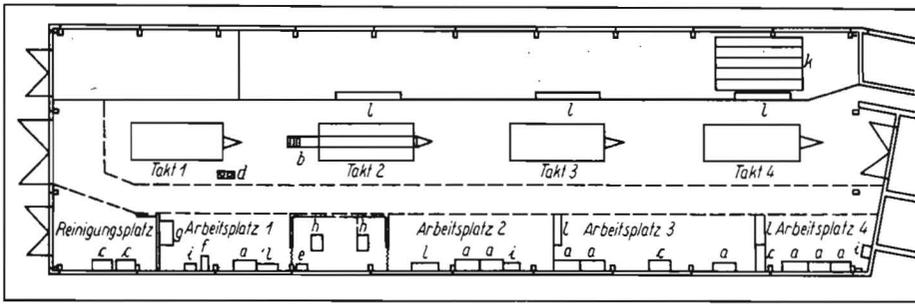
Maschinenaufstellungsplan der neuen Technologie der Instandsetzung von Getreidetrocknern; a Werkbank, b Montagegrube, c Teilwaschtisch, d A-Schweißgerät, e CO₂-Schweißgerät, f Bohrmaschine, g Richtplatte, h Schweißstisch, i Schleifmaschine, k Lagerständer für Dächer, l Regal
